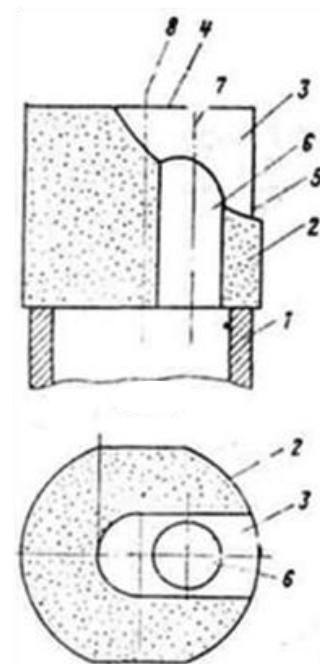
Конструкція алмазного свердла на металевій зв'язці
